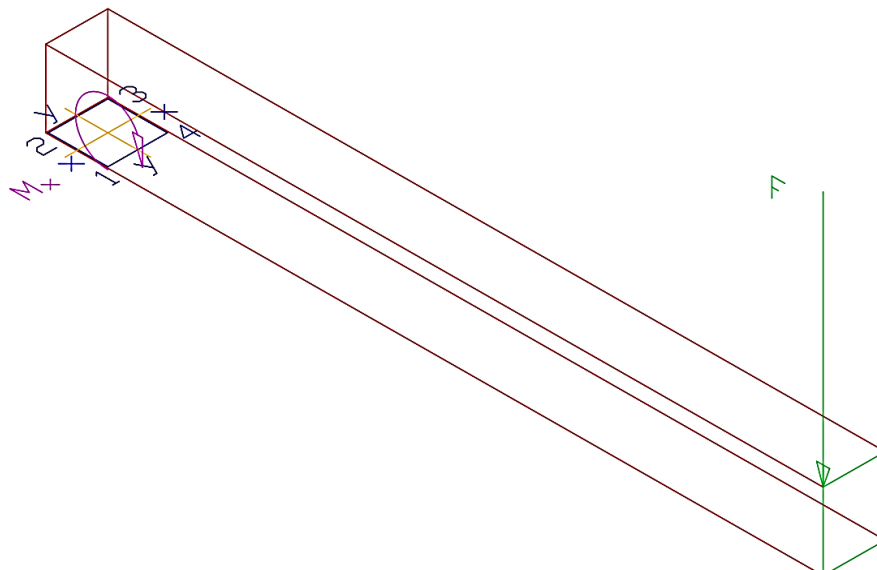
Diagrama de fuerzas que actúan sobre cordón de soldadura
